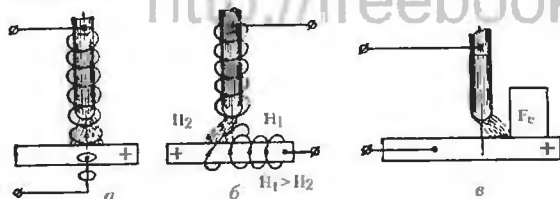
Вплив магнітного поля на зварювальну дугу:
